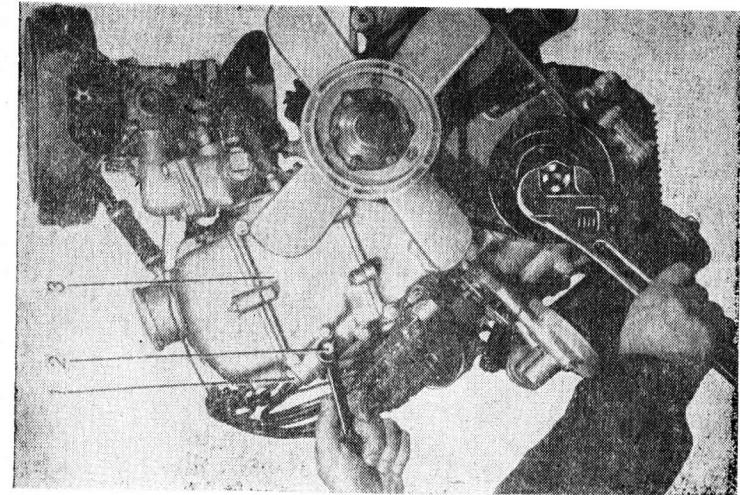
Регулировка натяжения цепи привода газораспределения:
